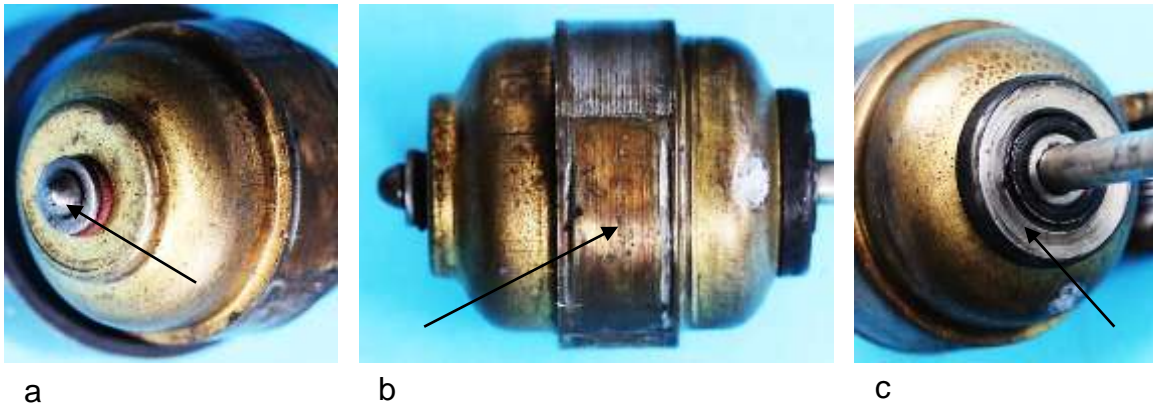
Ankeransichten: a) Spannung führender Kontakt, b) Mit den Verschlusskappen verlötetes Pollückenblech, c) Masseschleifring
